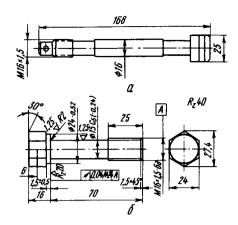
Шатунные болты: a — компрессора АУ200;  $\delta$  — компрессора П110
